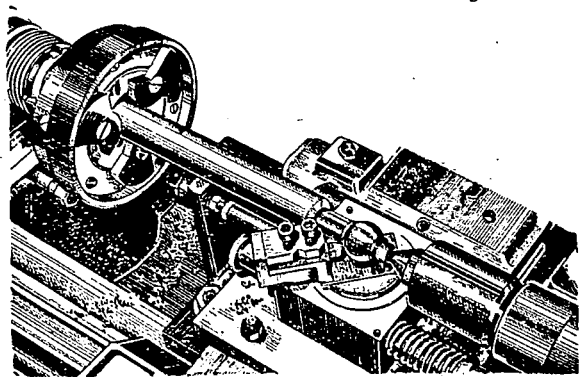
Приспособление с вращающимся столом для обработки сферических поверхностей, установленное на станке.
